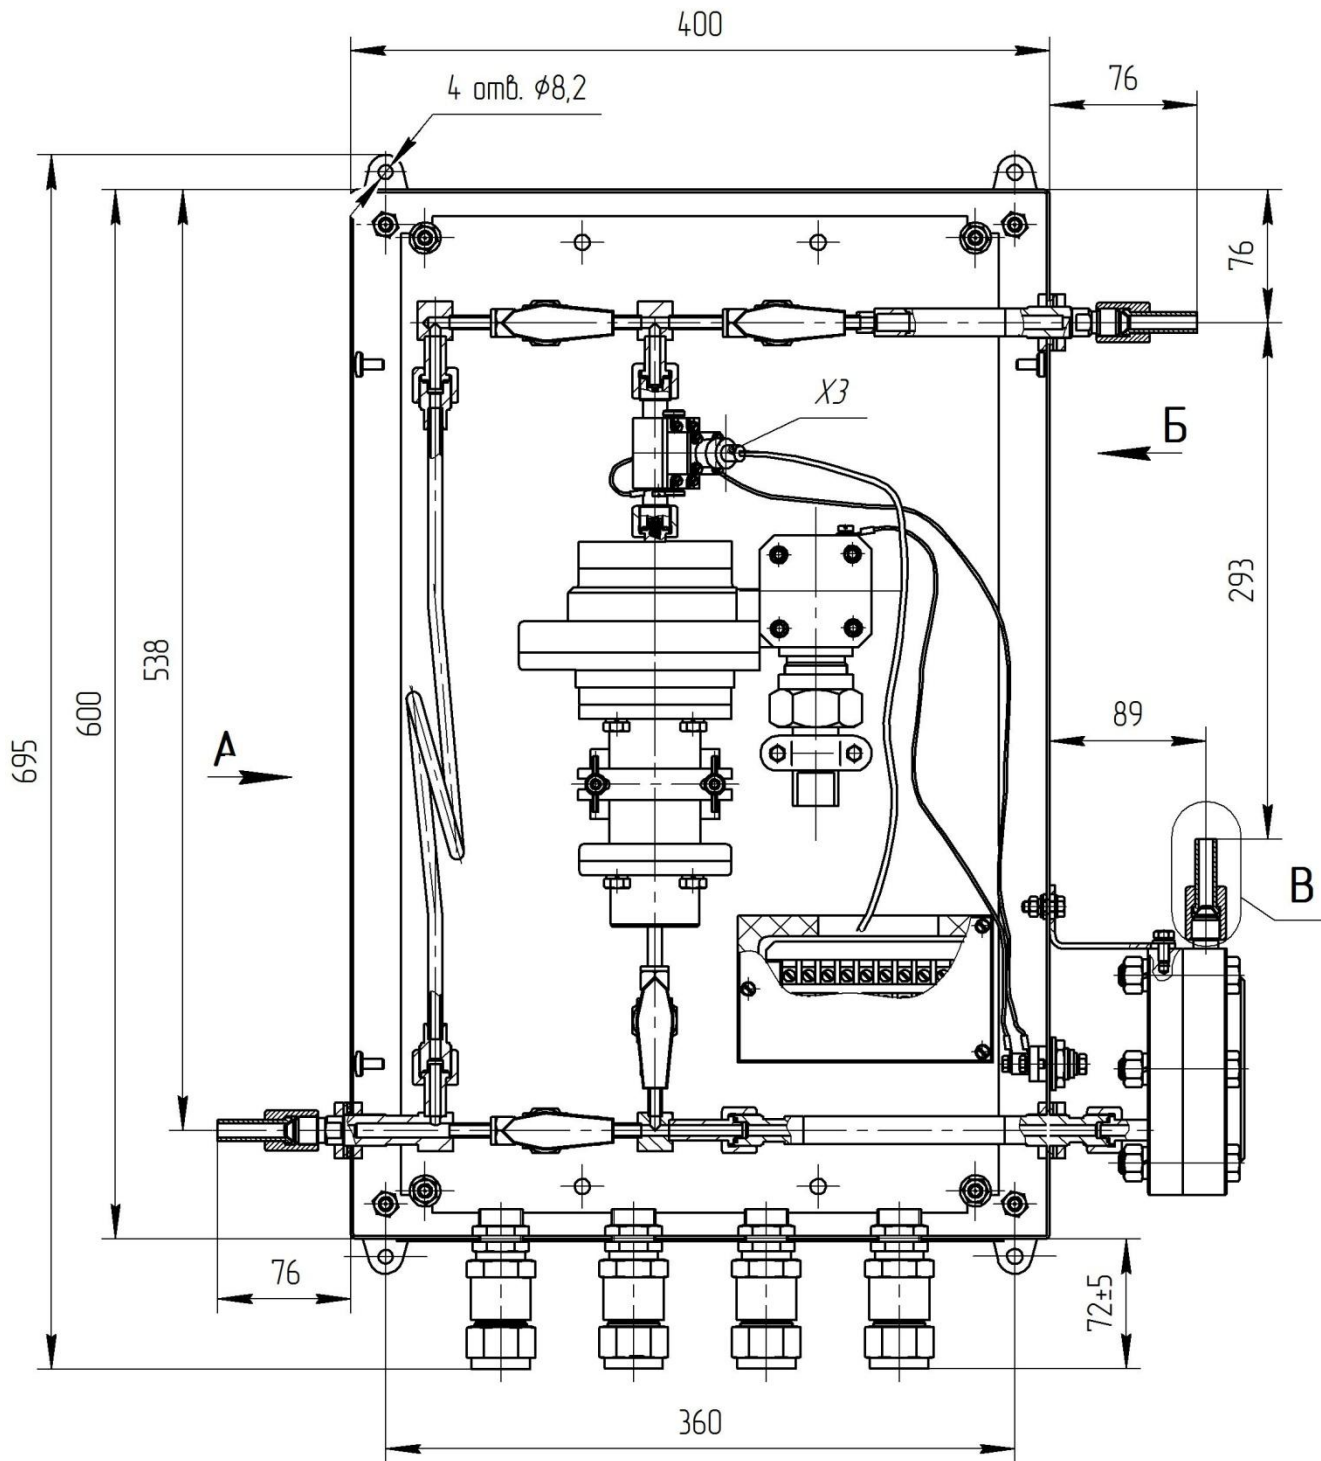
(лист 1 из 2) – Габаритные и присоединительные размеры дозатора
